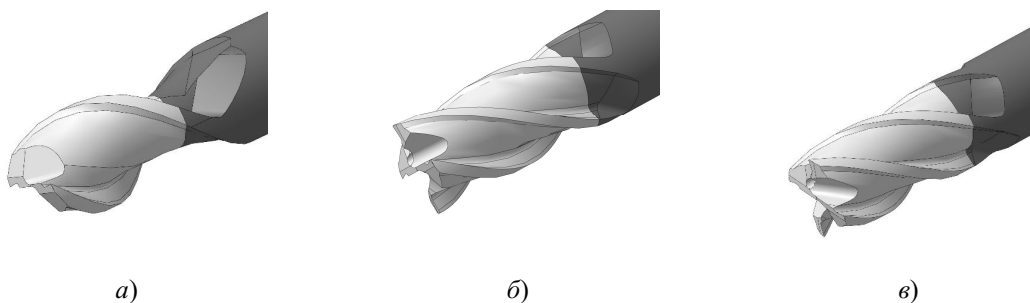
3D-модели фрез: с двумя режущими зубьями (а); с увеличенным диаметром (б); с углом винтовой канавки, равной 38° (в)
